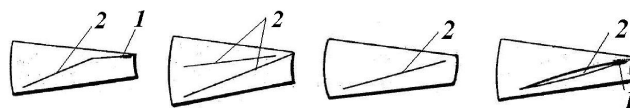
Види початкових заготовок у формі секторів із прорізами: 1 – зварний шов; 2 - проріз
